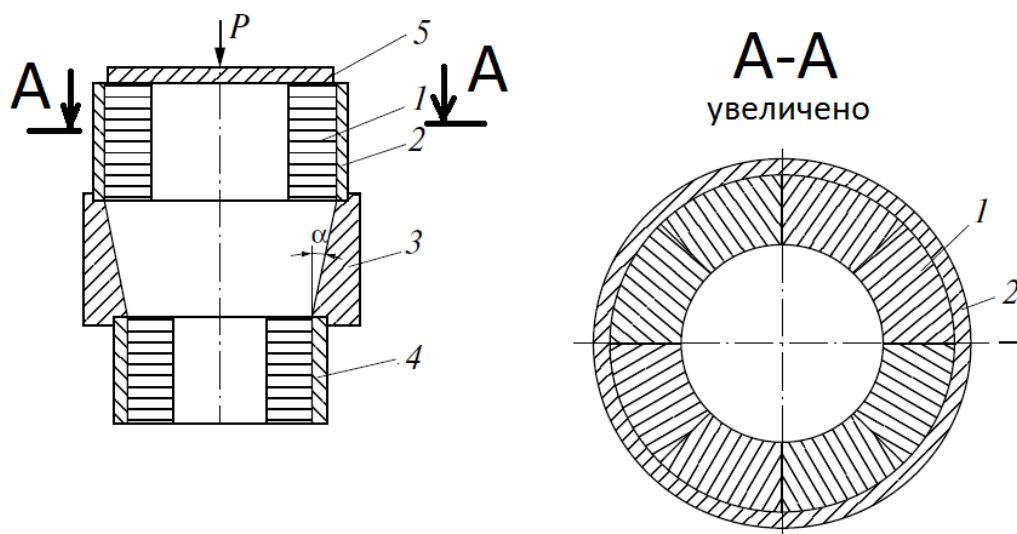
Схема запрессовки подшипника: 1 – сегменты; 2 – вспомогательная обойма; 3 – конус; 4 – окончательная обойма; 5 – пуансон
